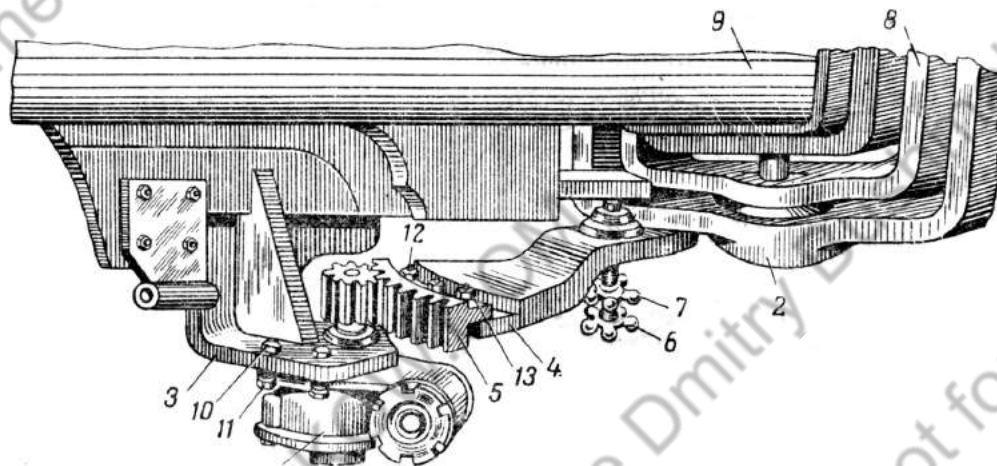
Поворотный механизм. Общий вид (снизу, слева):
